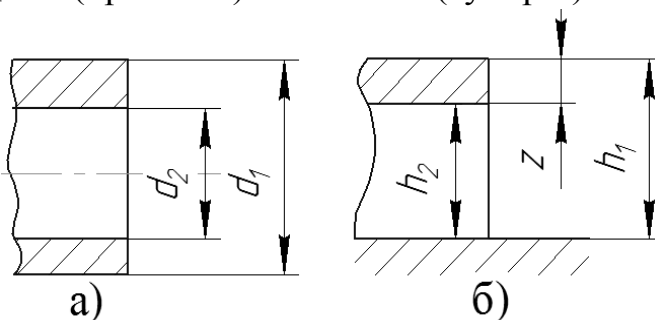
Розміщення припуску на поверхні деталі обертання (а) і на плоскій поверхні (б)
